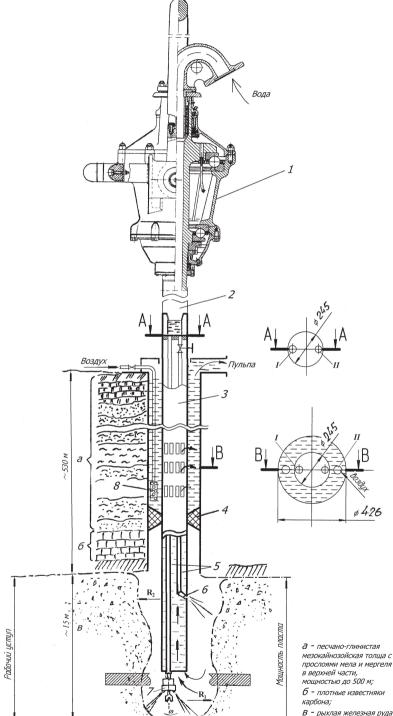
Схема гидродобычного агрегата ГДА-600 с эрлифтной установкой для подъема пульпы: 1 — вертлюг; 2 — ведущая труба; 3 — добычная колонна; 4- пакер; 5- трубопроводы I и II; 6- гидромонитор; 7- буровое долото с двумя гидромониторами; 8 — эрлифтная установка
